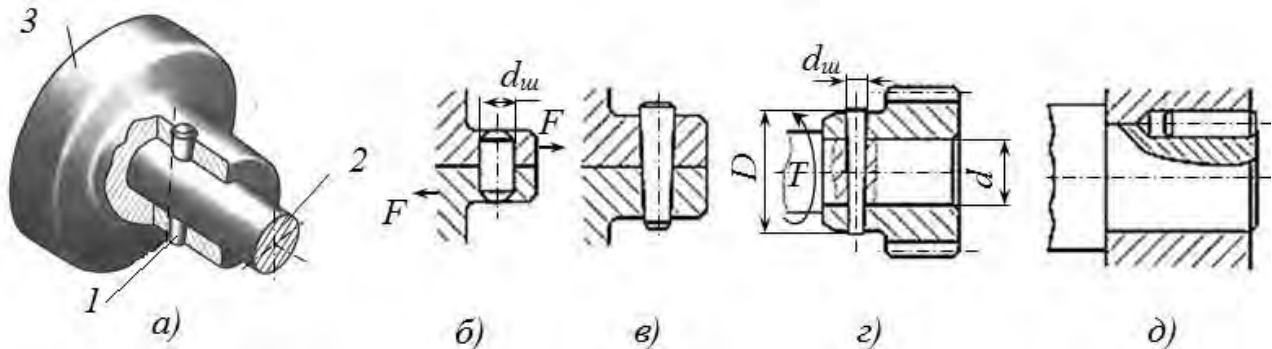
Штифтові з'єднання: загальний вигляд (а), схеми з'єднань штифтами (б - д): 1 – штифт; 2 – вал; 3 – маточина деталі
